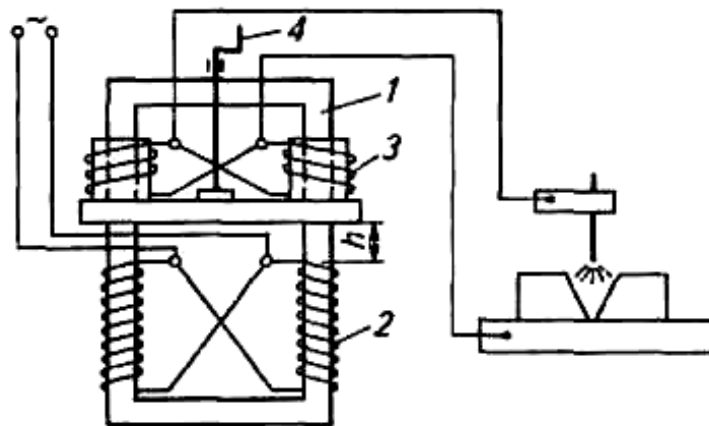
Схема сварочного трансформатора ТД-300: 1 – сердечник (стержневой магнитопровод); 2 – первичная обмотка; 3 – вторичная обмотка; 4 – ходовой винт
